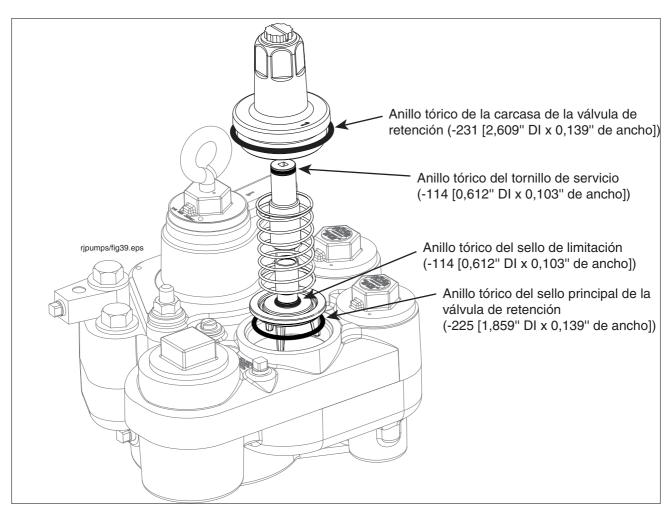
Inserción del conjunto de la válvula de retención en el colector
